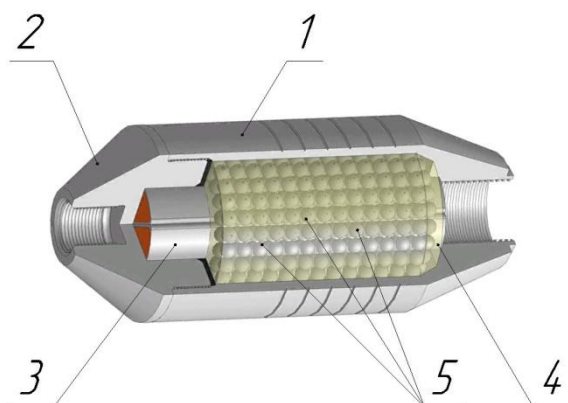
Схема боеприпаса предлагаемой конструкции:
